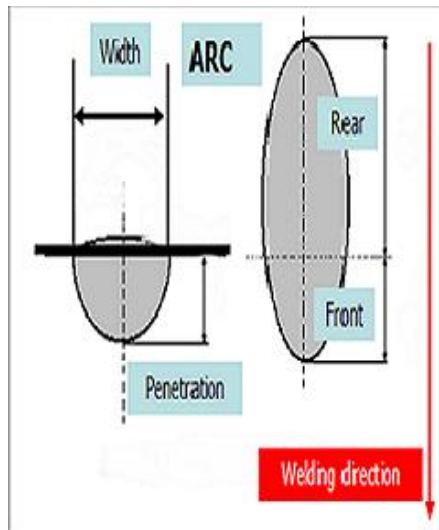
Propriedades físicas de um cordão de soldadura por arco elétrico.
